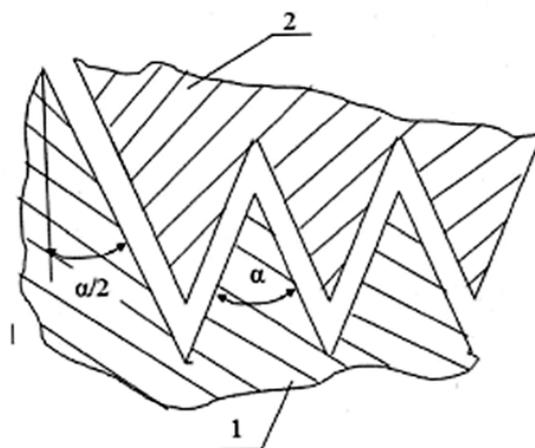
Схема выступов и впадин диспергатора: 1 – корпус; 2 – ротор
